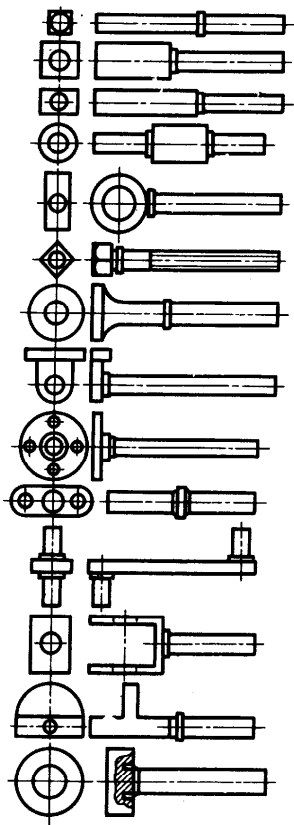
Детали автомобилей, изготовленные с применением сварки трением
